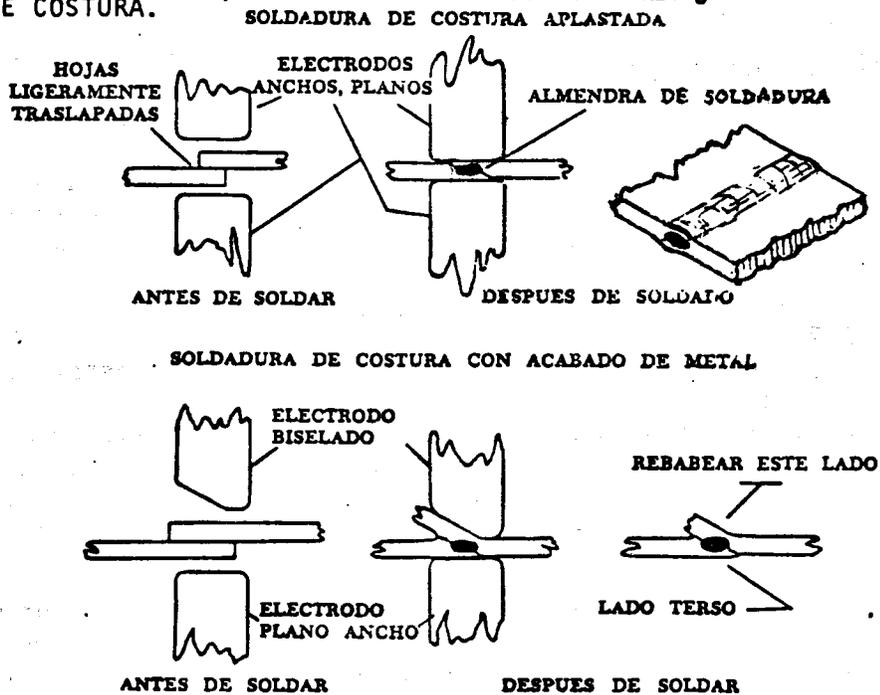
TIPOS DE SOLDAURA DE COSTURA.
